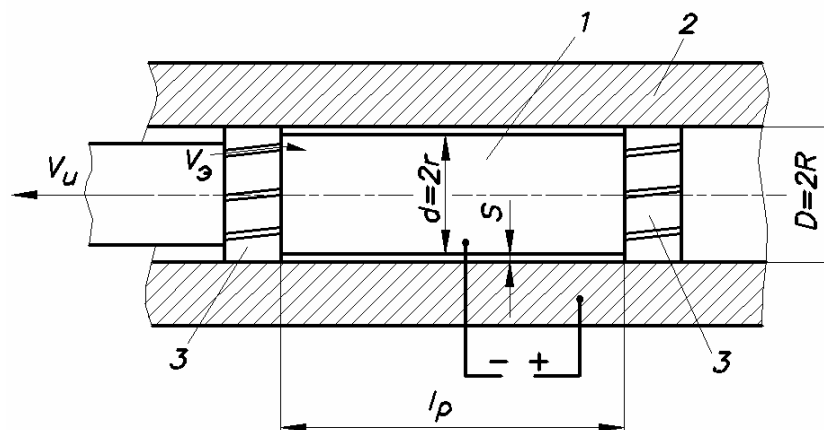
Схема протягивания внутренних поверхностей:
